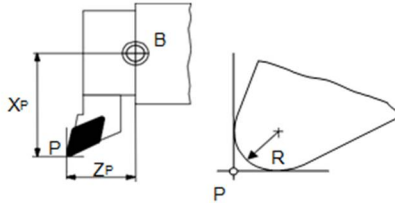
Розташування точки установки інструменту на токарному верстаті з ЧПК
